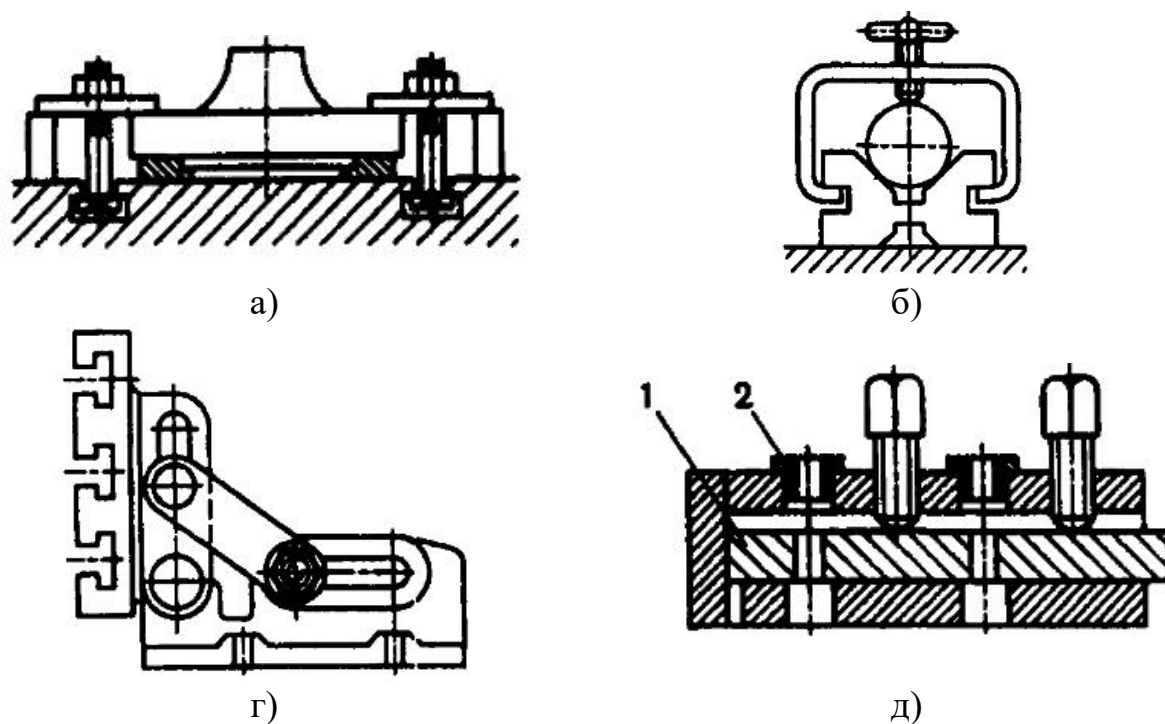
Пристосування для закріплення заготовок на свердлильних верстатах
